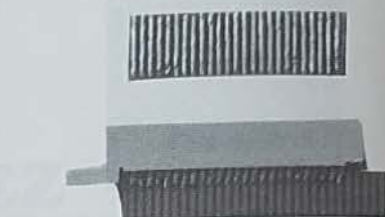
Connecteur 60 pistes soudé à l'arrière du connecteur Card Edge
